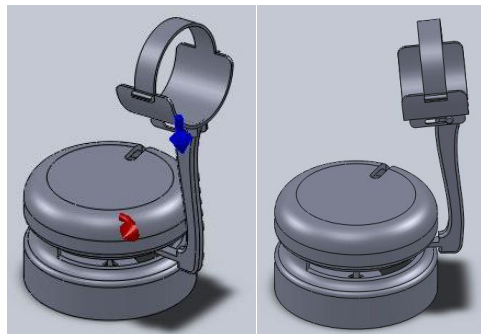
Propuesta de diseño de mecanismo para realizar la flexo-extensión de la pierna arrastrando la tibia-peroné. Solidworks©
